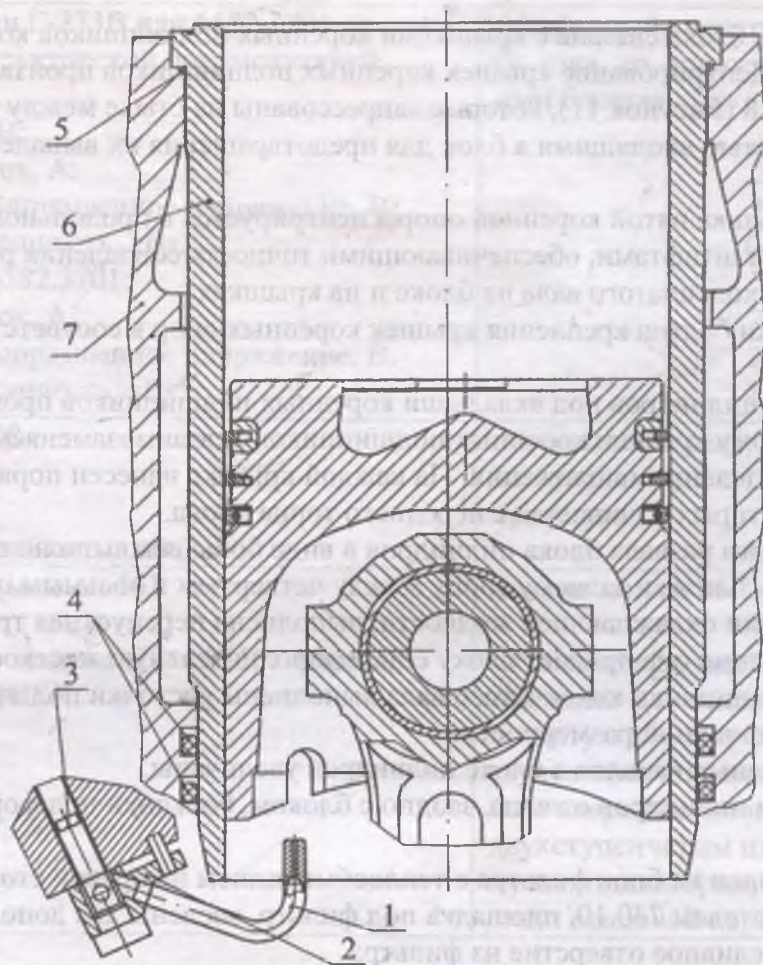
Установка гильзы цилиндра и уплотнительных колец
